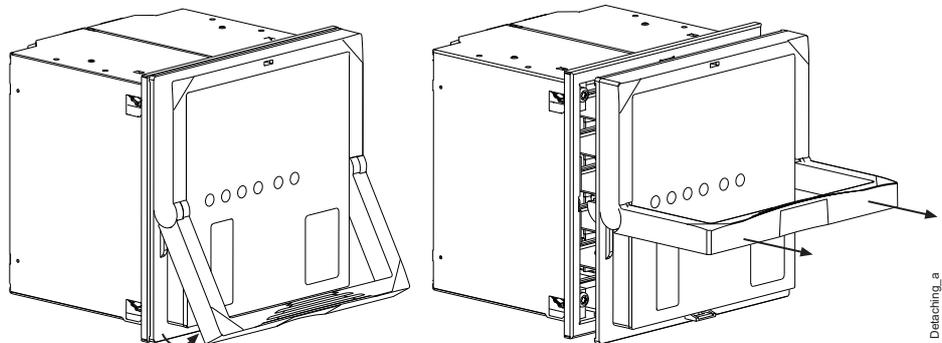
1 Separación de la unidad enchufable de la caja
